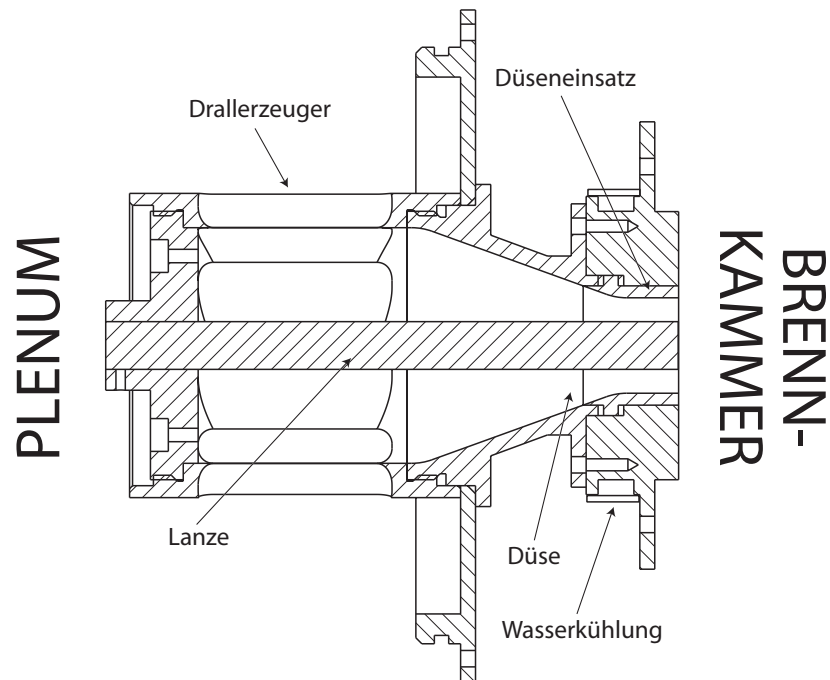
Querschnitt des TD¹ Brenners mit 32 mm Einsatz für die Austrittsdüse
